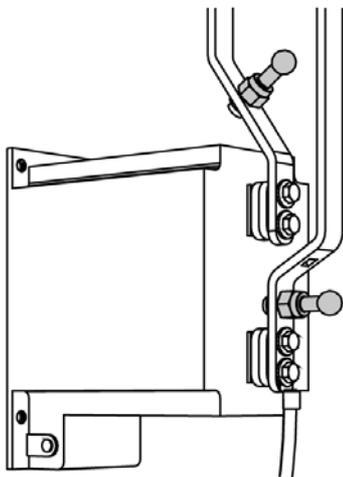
Заземляющая шпилька для ячейки типа сборная шина-сборная шина
